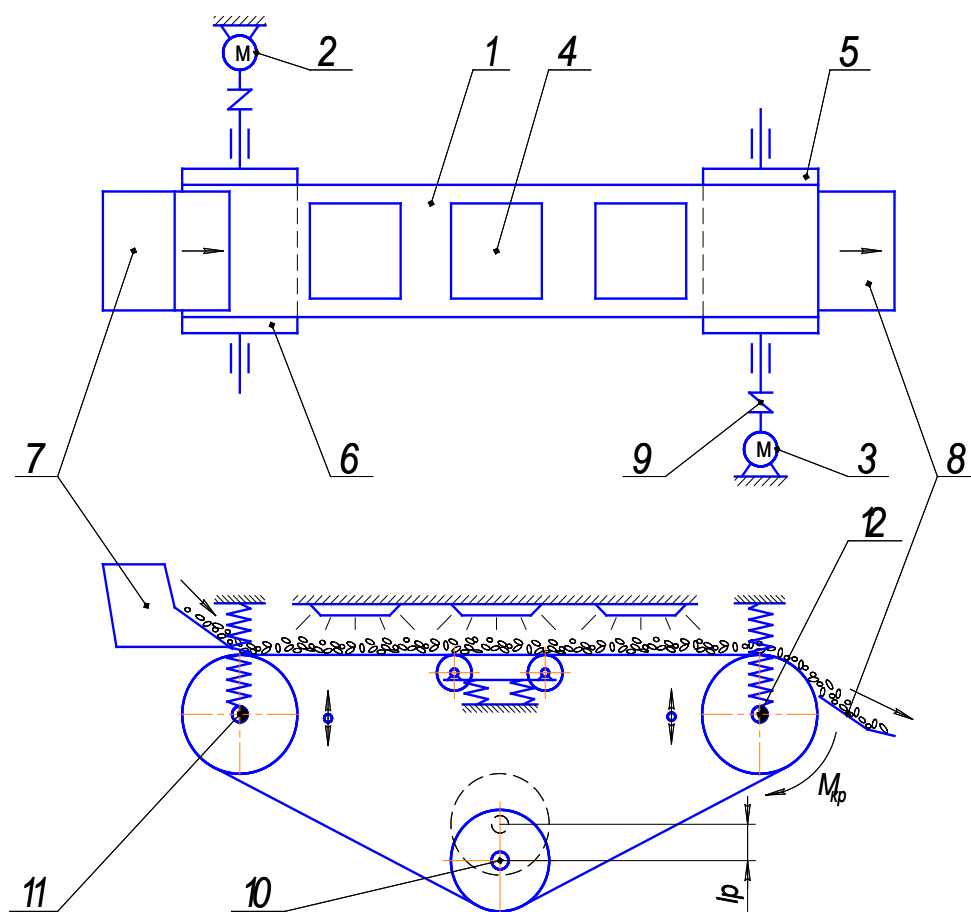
Принципова схема віброконвеєрної інфрачервоної сушарки: 1 – стрічка; 2, 3 – двигуни віброзбудувачів; 4 – інфрачервоні випромінювачі; 5, 6 – котки; 7 – живильник; 8 – приймальний бункер; 9 – гнучка муфта; 10 – натяжний коток; 11, 12 – дебалансні віброзбудувачі.
